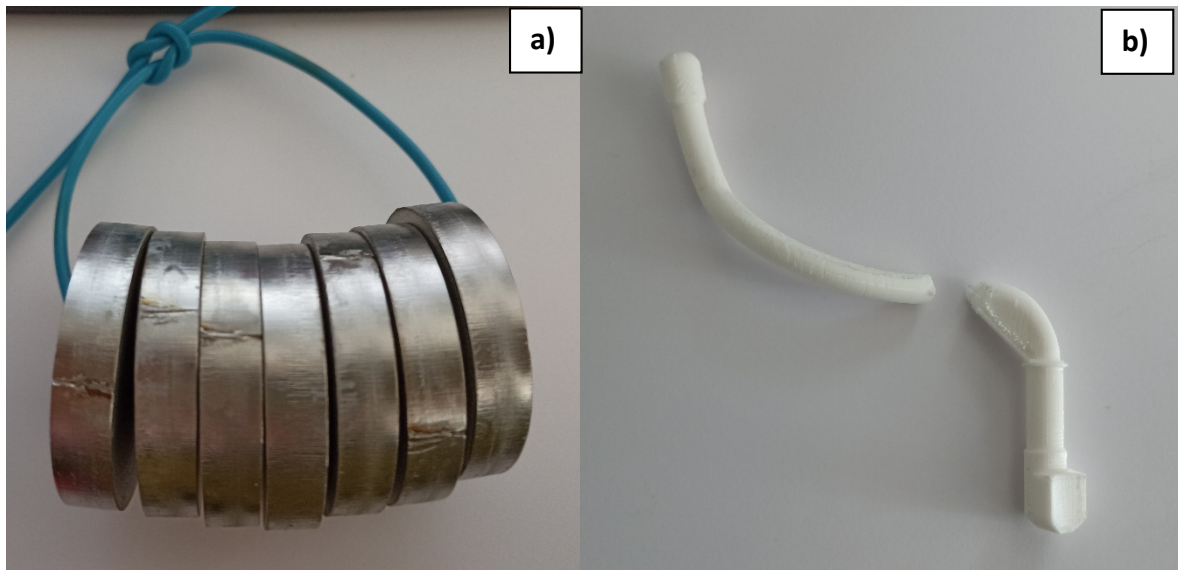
a) Peso para el primer ensayo de carga sobre el pulgar. b) Zona de la fractura.
